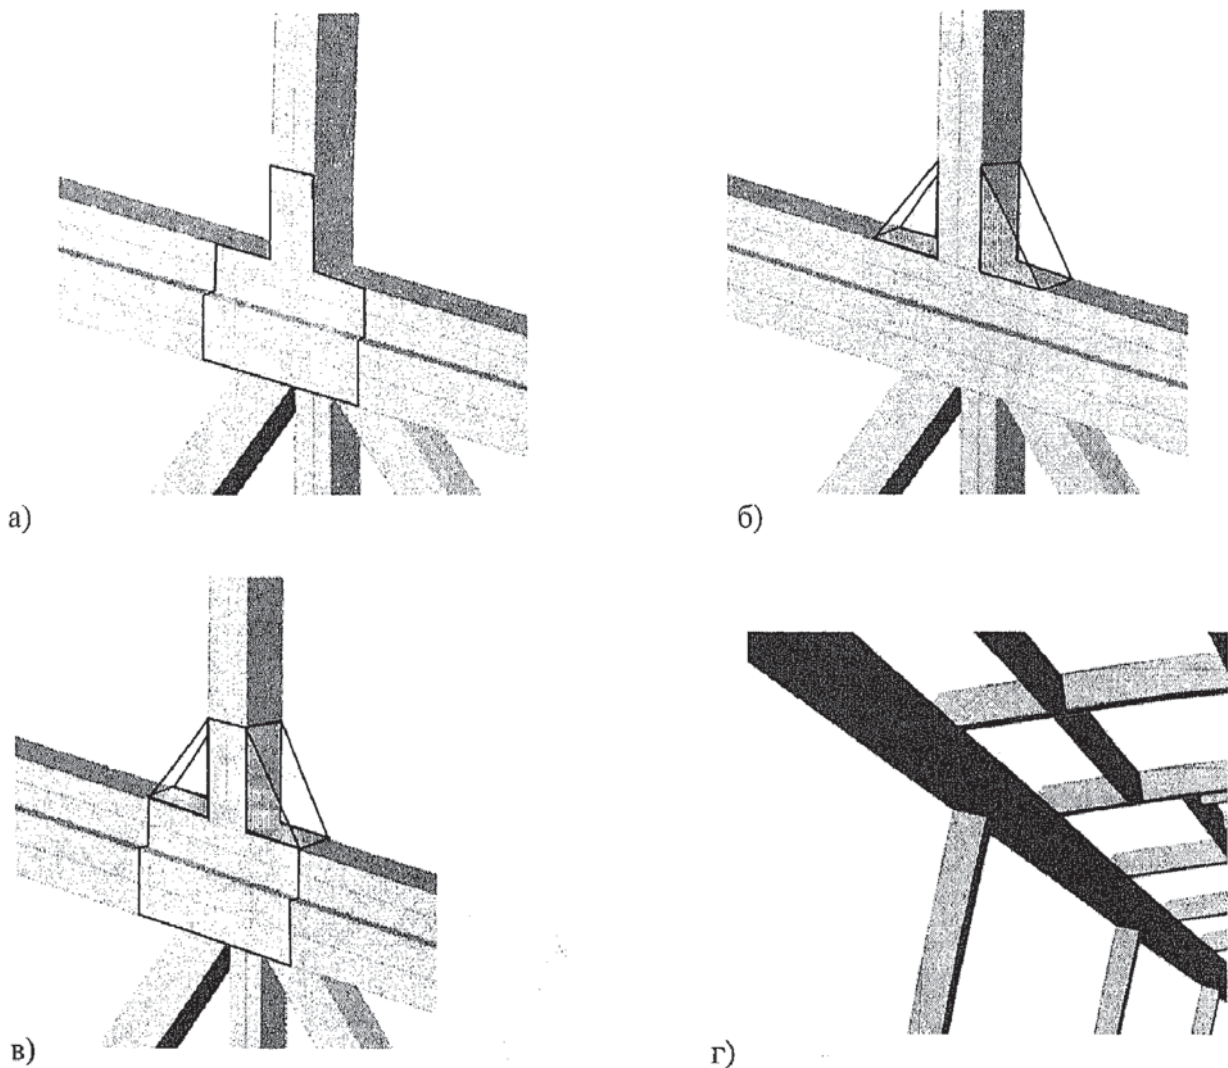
Варианты конструктивной доработки узлов крепления деталей корпуса автобуса: а) накладки; б) ребра жесткости; в) комбинированный вариант; г) упоры для балок крыши.
